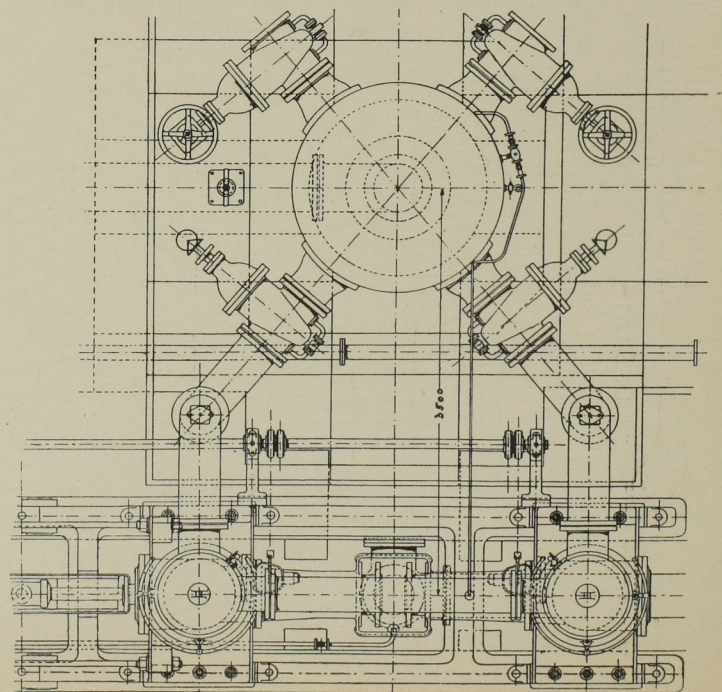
Grundriss und Rohrplan. Massst. 1:60.
